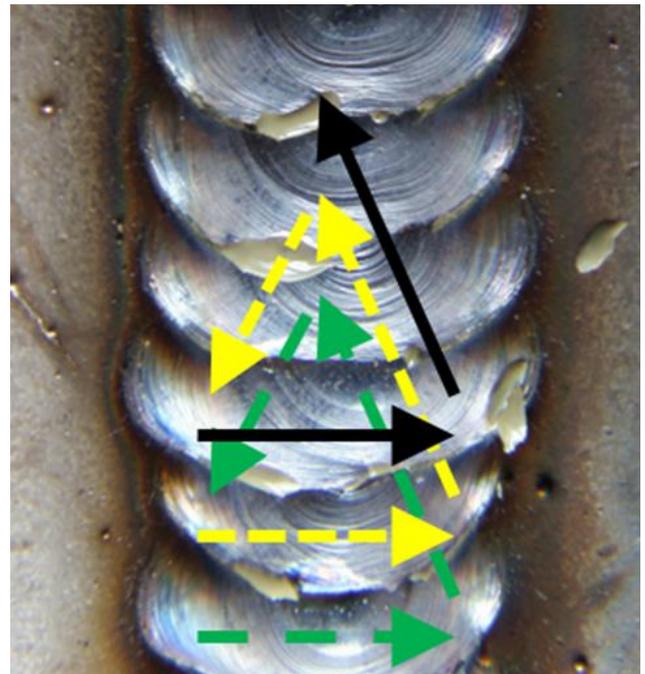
Steignacht zu hastig geschweißt (Stahl 8mm, M21, 1mm G3Si1)
